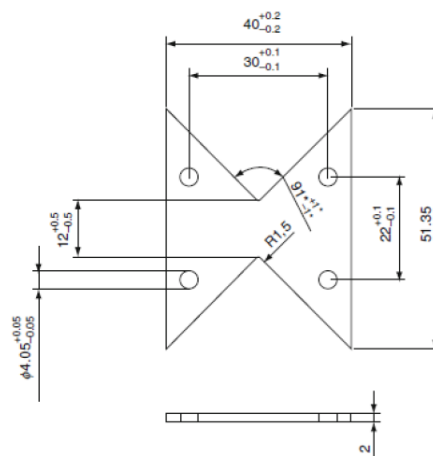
Geometria e dimensões (em mm) de um provete usado no teste Arcan [34]
